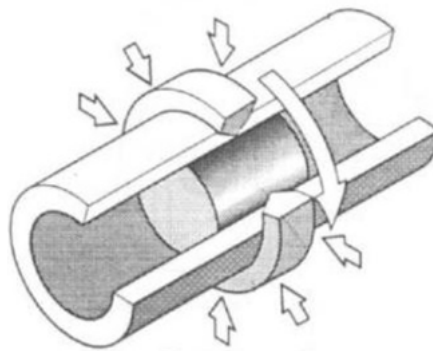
Soldagem por fricção radial<sup>(29)</sup>.
